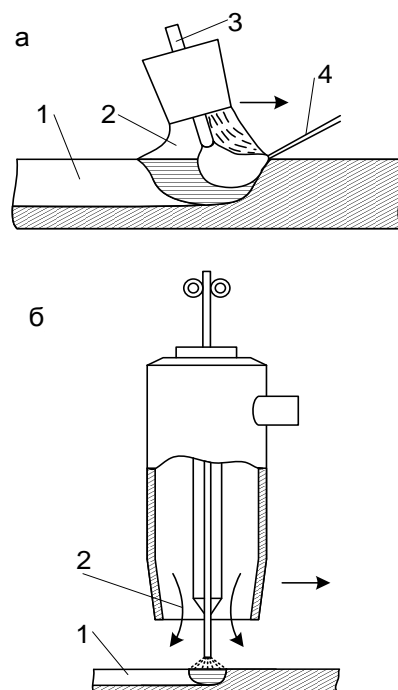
Схема дуговой сварки в защитном газе:
